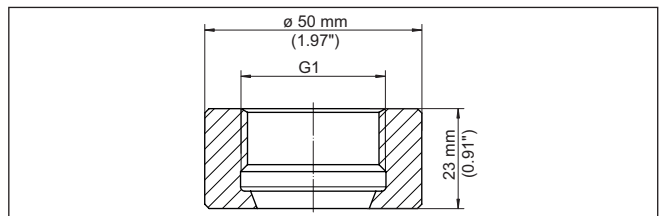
Dimensiones racor para soldar directo G1 (ISO 228-1) - Junta cónica
